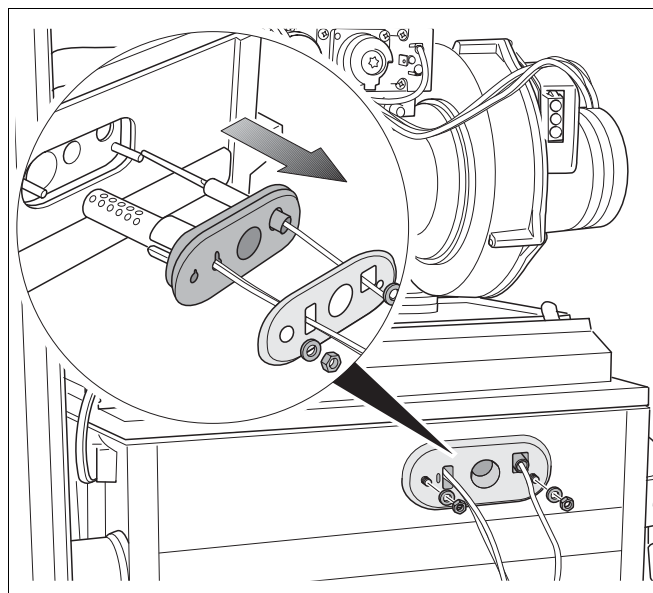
Demontați electrodul de ionizare și electrodul de aprindere
